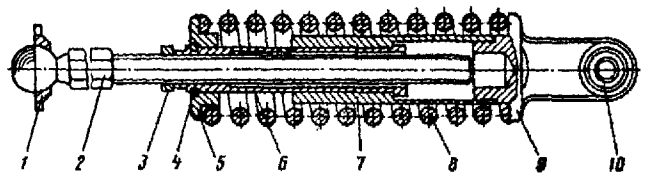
Амортизатор: 1 – крышка крепления амортизатора к нижней опоре; 2 – регулировочный винт; 3 – конусная гайка; 4 – полукольцо; 5 – нижняя опора; 6 – верхняя труба; 7 – наружная труба; 8 – пружина; 9 – верхняя опора; 10 – шарнир
